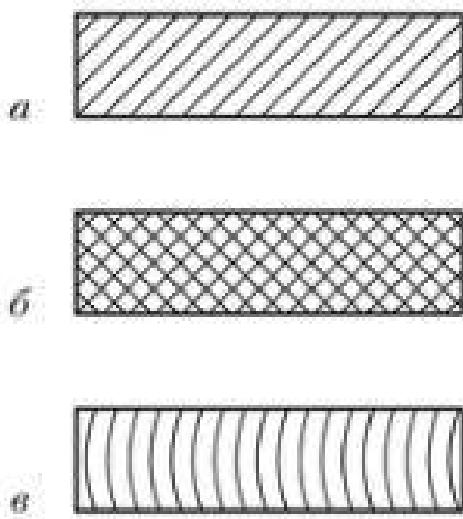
Виды штифтовки деталей в сечениях и разрезах:
